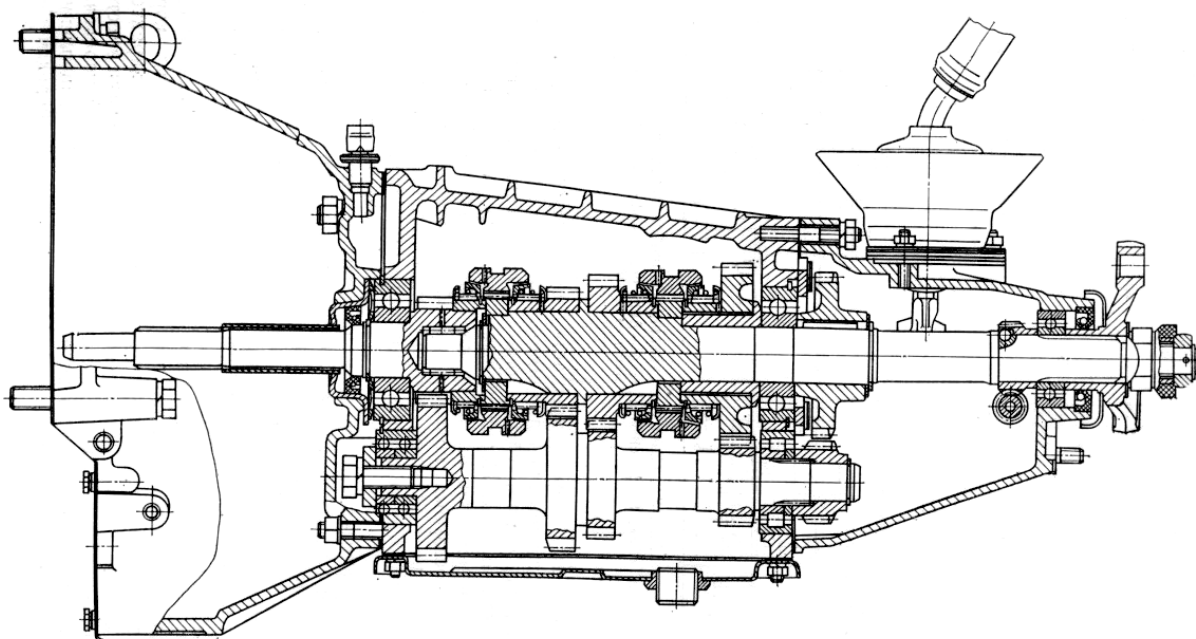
Конструкция коробки передач автомобиля ВАЗ-2101
